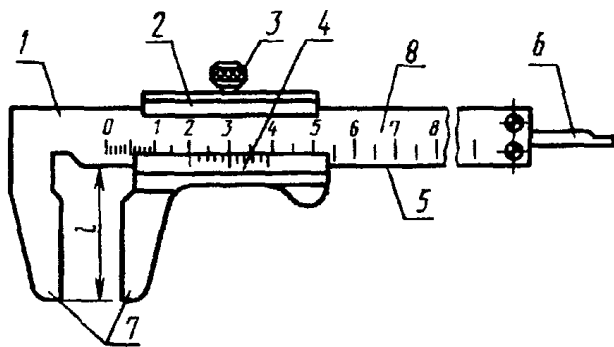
1- штанга; 2- рамка; 3- зажимаючий елемент; 4- ноніус; 5- робоча поверхня штанги; 6- глибиномір; 7- губки з плоскими вимірювальними поверхнями для вимірювання зовнішніх розмірів; 8- шкала штанги
